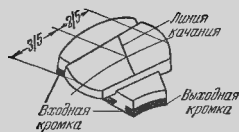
Новое расположение опорного ребра на сегменте упорного подшипника.
